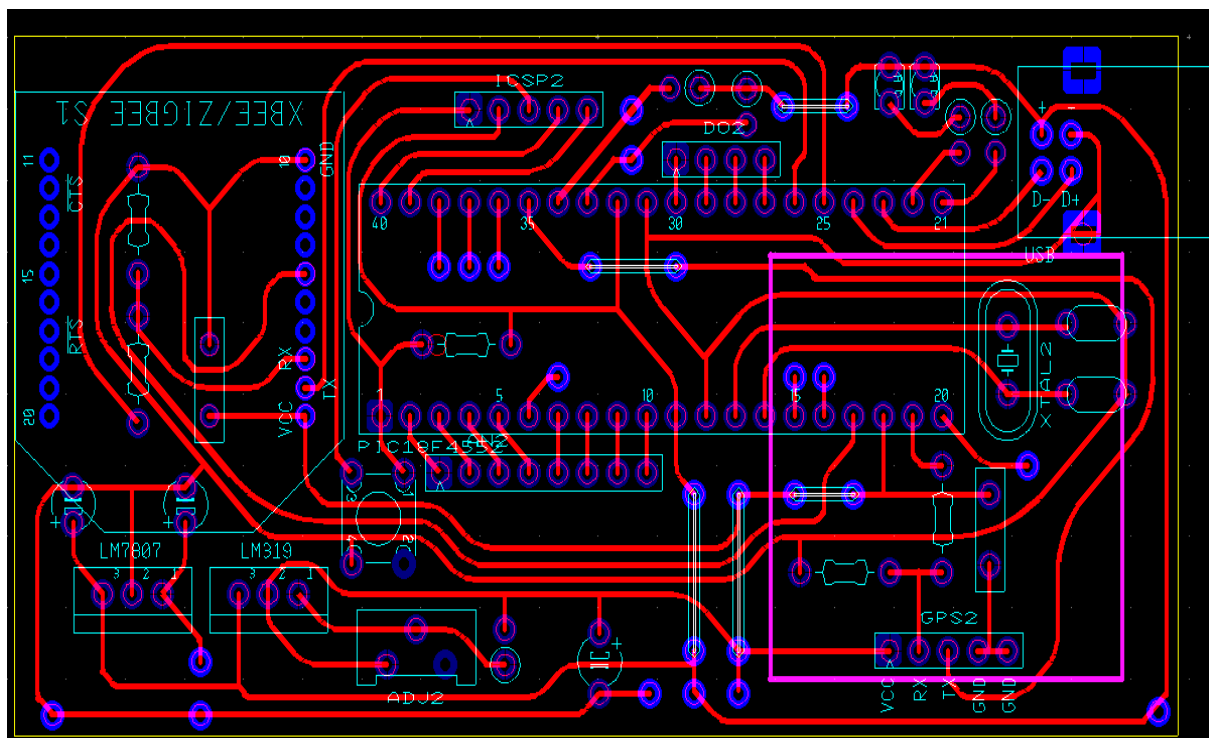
Leiaute de PCB do dispositivo móvel.
